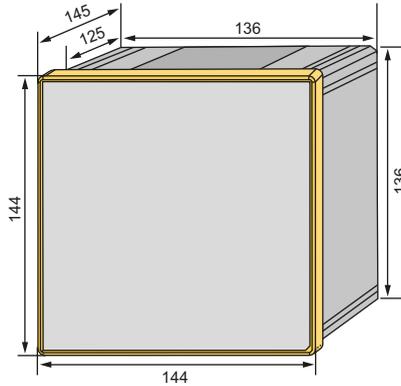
Maßbild PEM735 (Frontansicht)
